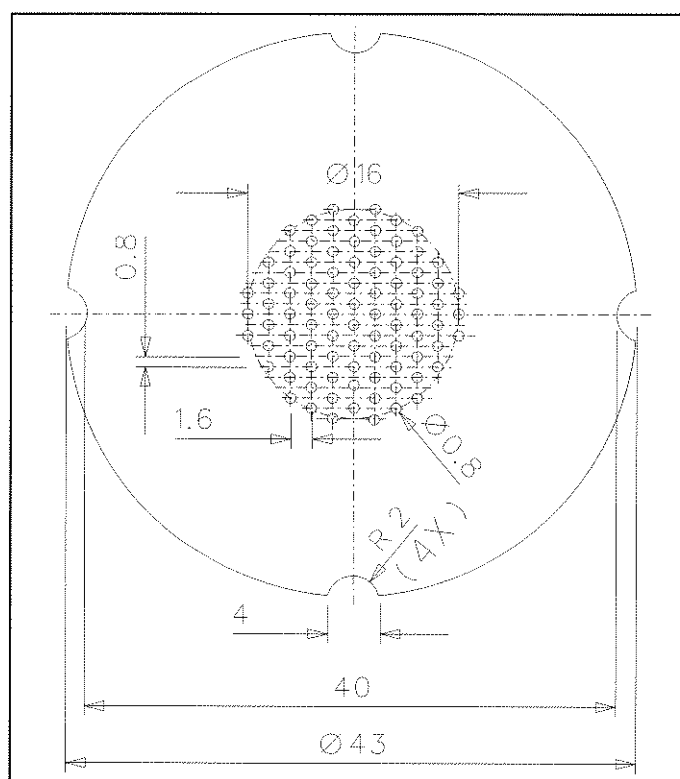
Desenho mecânico do catodo de níquel (dimensões em mm).
